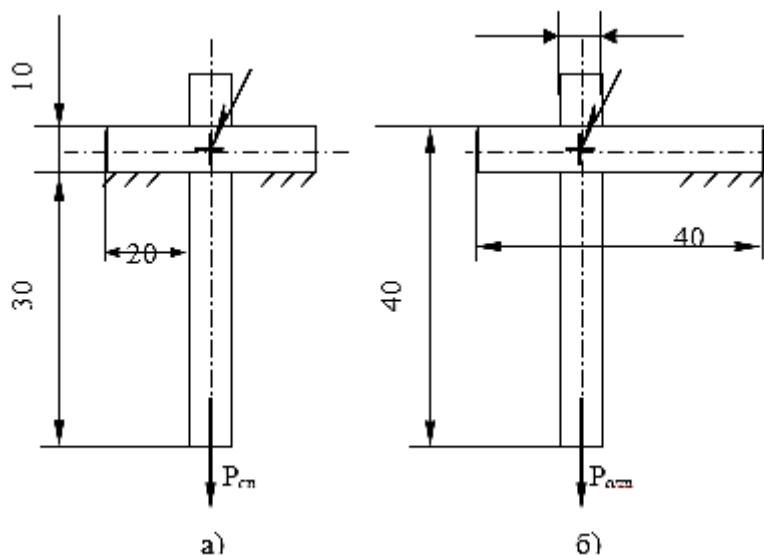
Схемы испытания сварных соединений на срез (а) и на отрыв (б)
